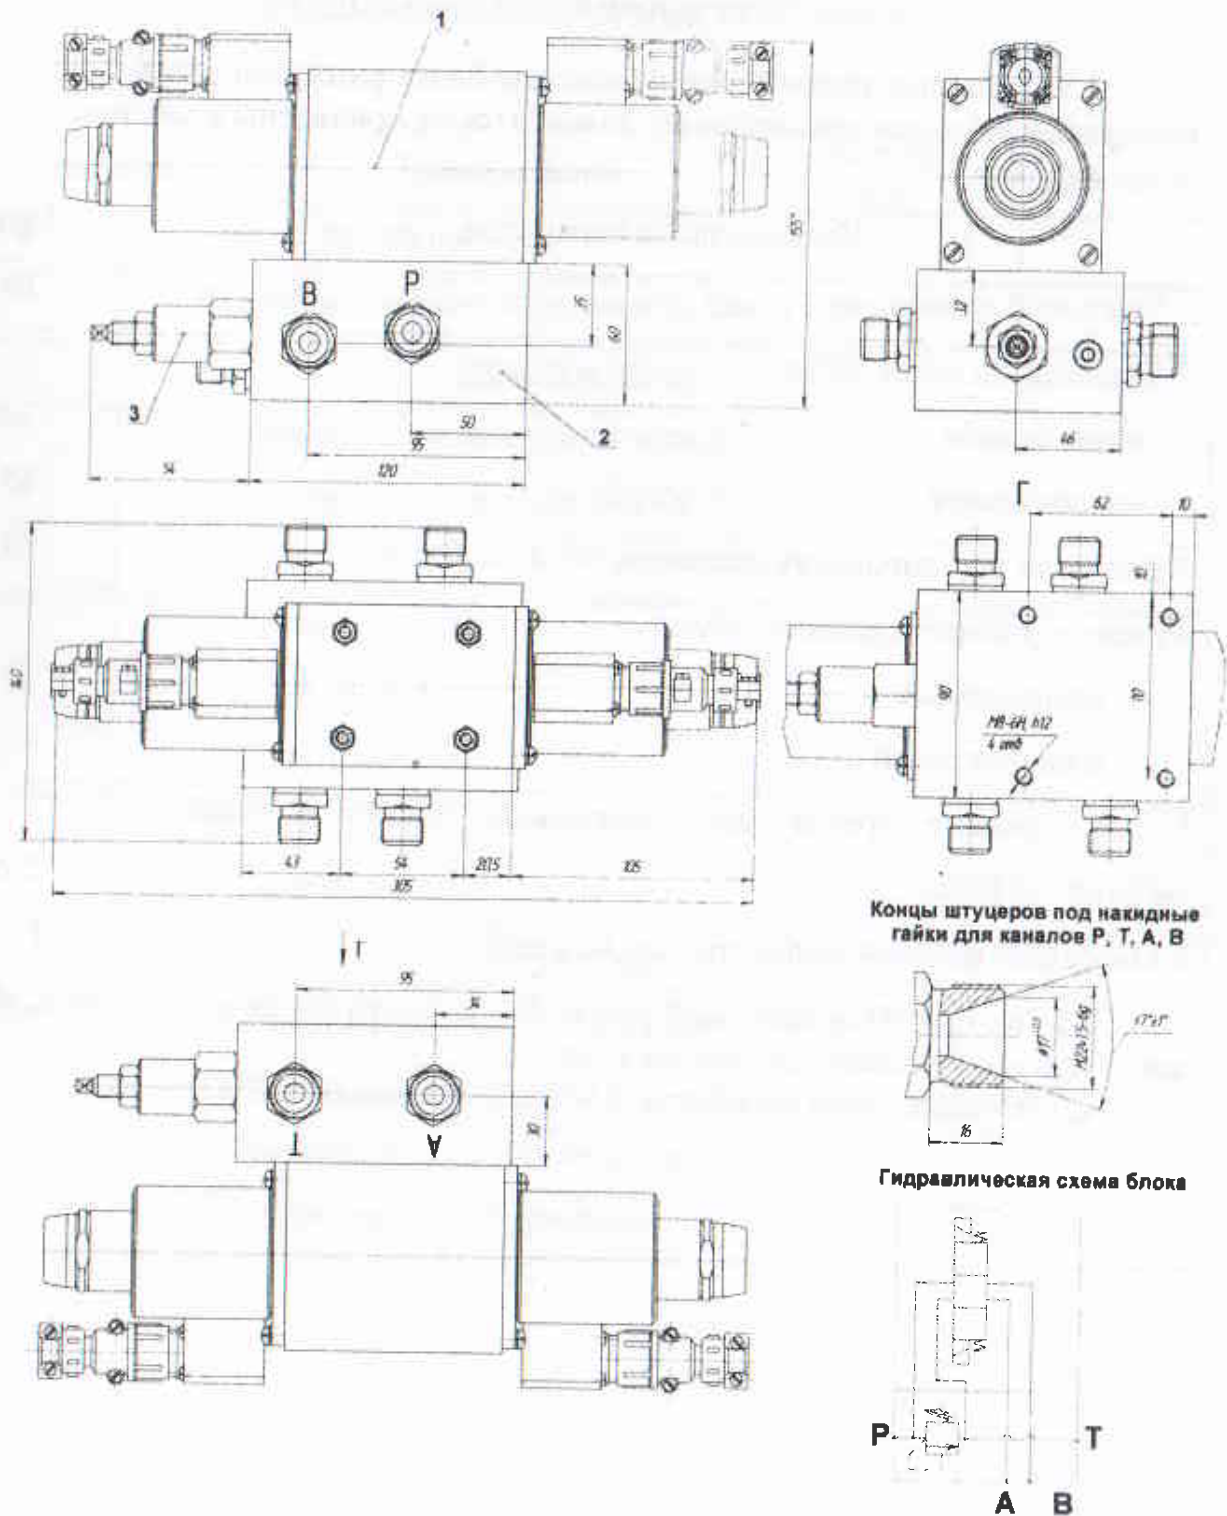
Габаритные и присоединительные размеры блока разгрузки
